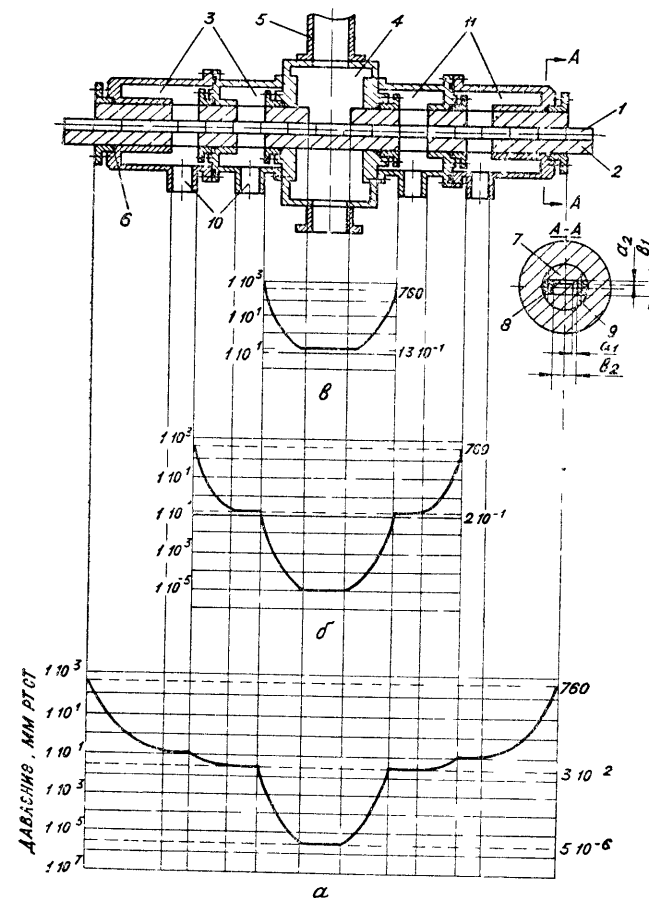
Конструкция рабочей камеры и шлюзового загрузочного устройства для непрерывной подачи изделий из атмосферы в рабочую камеру:
